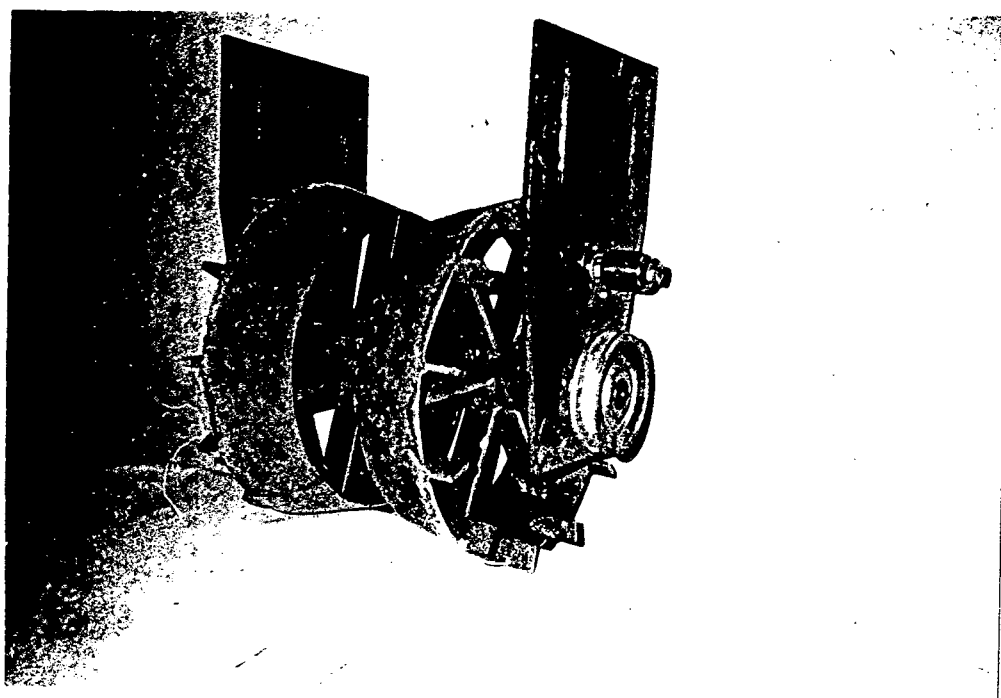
Conjunto compactador visto de um outro ângulo.
